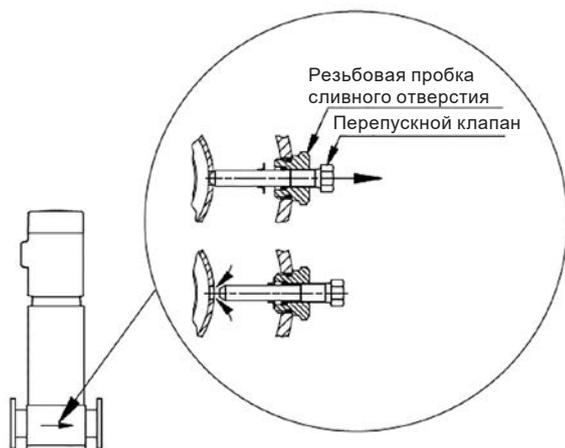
Местоположение резьбовой пробки сливного отверстия с перепускным клапаном
